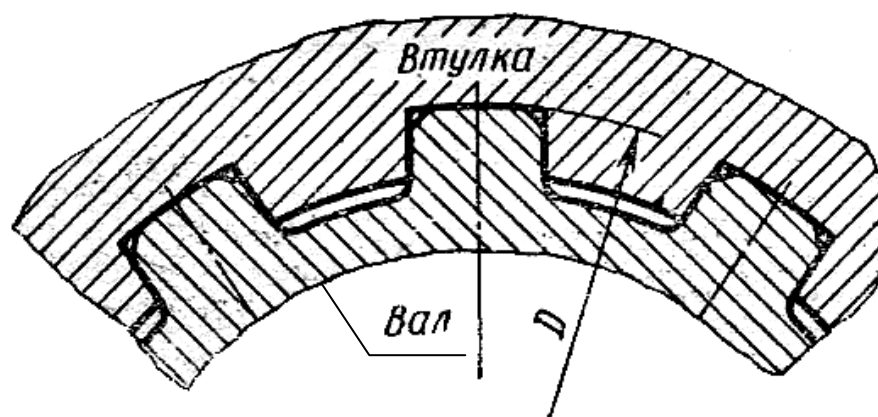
Центрирование по диаметру вершин зубьев вала (D)
